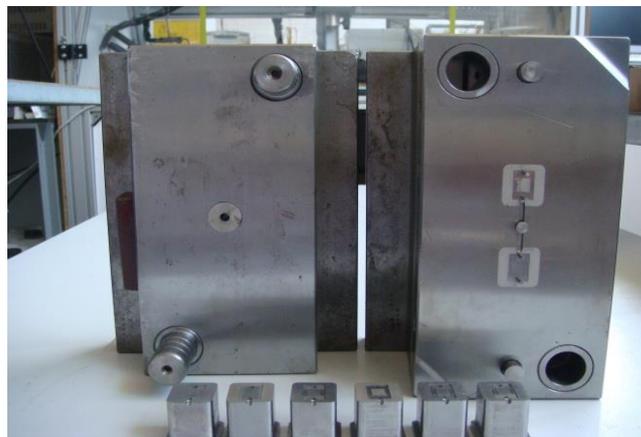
Ferramenta de moldagem com inserções revestidas a diamante
